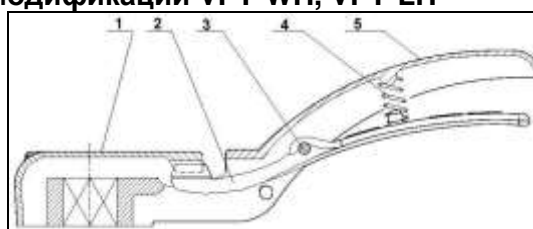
Устройство рукоятки. (1 – крышка; 2 – рычаг; 3 – шпилька; 4 – пружина; 5 – рычаг)
